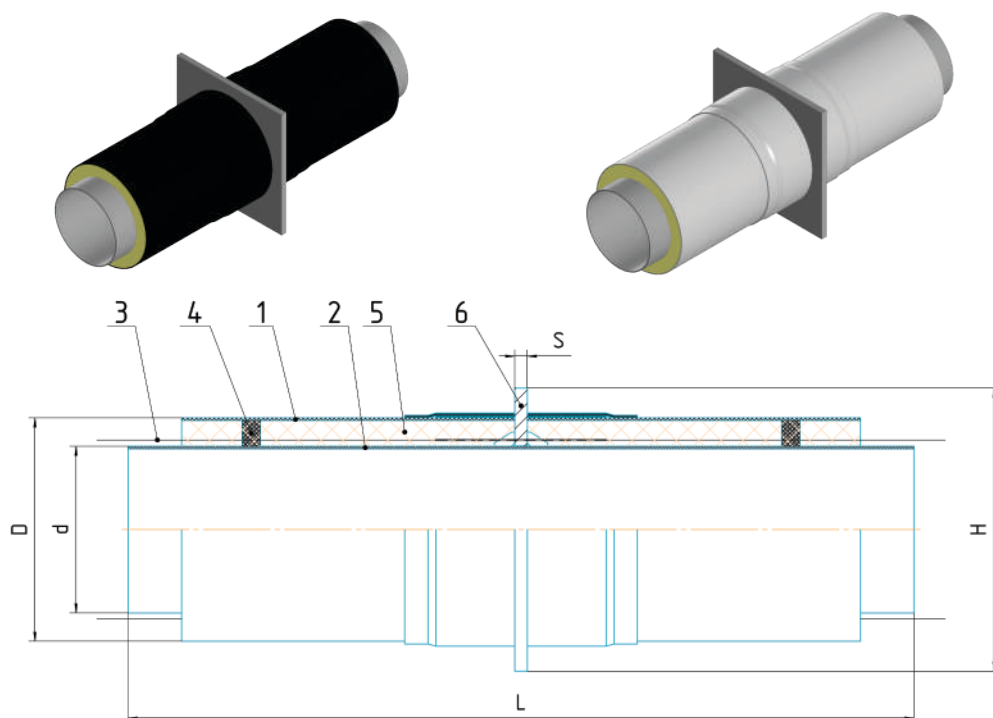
Конструкция неподвижной опоры трубопровода
